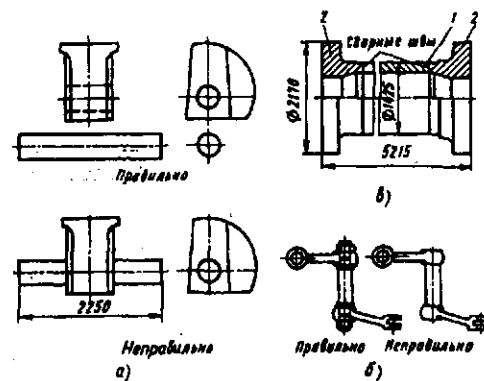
Примеры замены поковок сложной формы сварными или составными из частей
